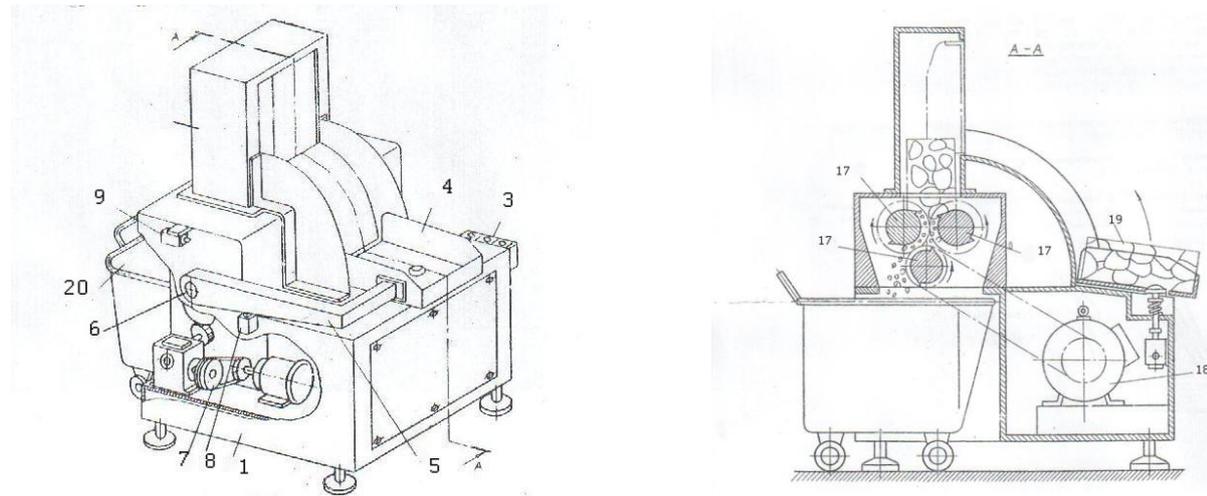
Устройство для измельчения мясных мороженных блоков
